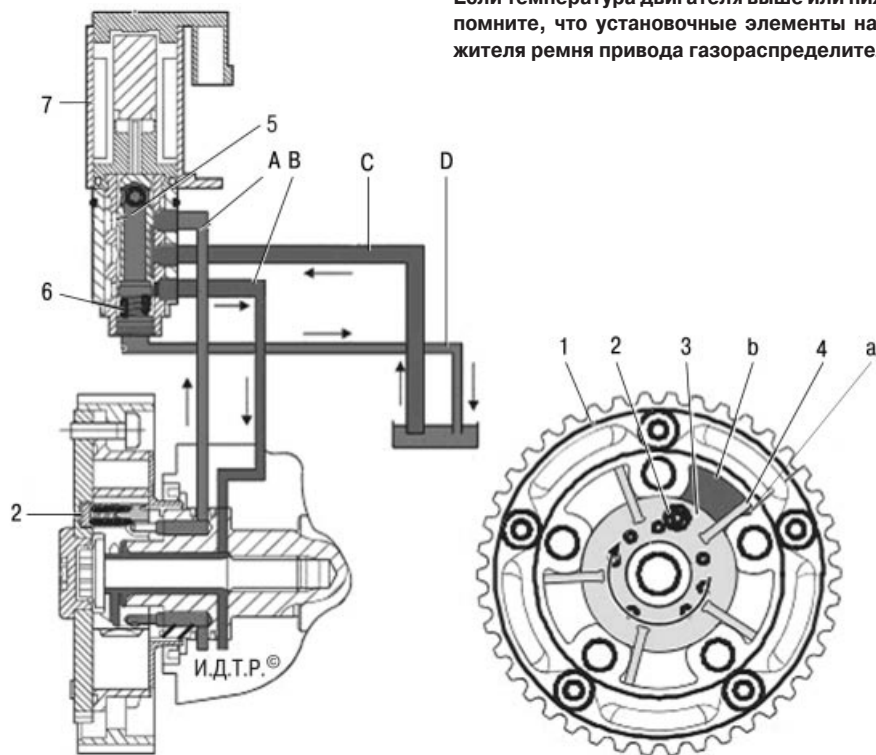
Схема работы электромагнитного клапана управления подачей масла: 1 – шкив механизма изменения фаз газораспределения; 2 – подпружиненный стопорный штифт; 3 – ротор; 4 – лопасть ротора; 5 – плунжер; 6 – возвратная пружина; 7 – электромагнитный клапан управления подачей масла VCT; А – канал, подсоединенный к камере а; В – канал, подсоединенный к камере b; С – канал подачи масла; D – канал возврата масла
